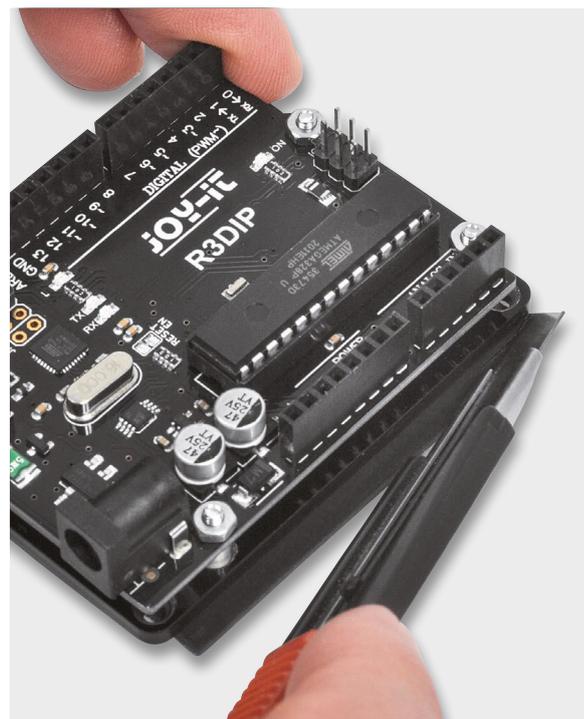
Überstehende Magnetfolie wird mit einem Cuttermesser abgeschnitten.
